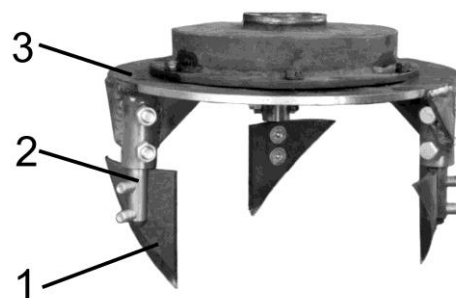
Загальний вигляд і ножовий ротор фрезерної машини:
